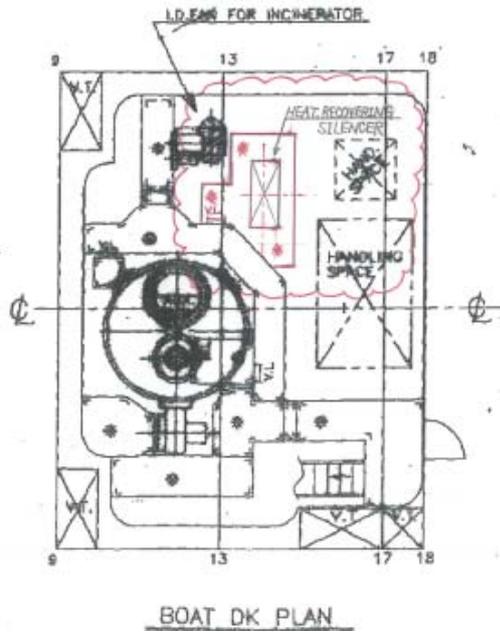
排熱回収型サイレンサ配置図(平面図) ※雲マークは改造箇所
